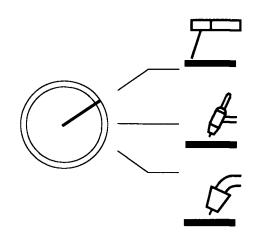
工艺选择开关(MMA 焊、TIG 焊、MIG 焊)
